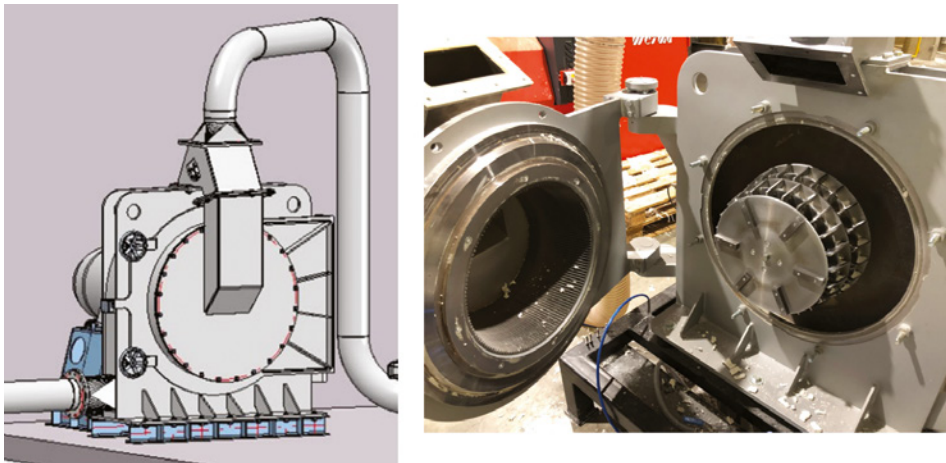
Links: Schema des Dry Pulpers. Rechts: geöffneter Dry Pulper mit Blick auf die Rotor-Stator-Garnitur (Quelle: TBP Future GmbH, Gotic GmbH)
